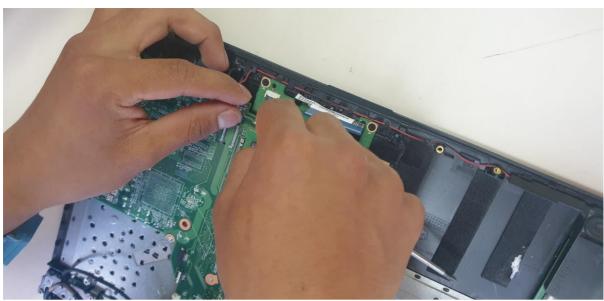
Desmontaje del cable de audio y Flex de Touch Pad.
